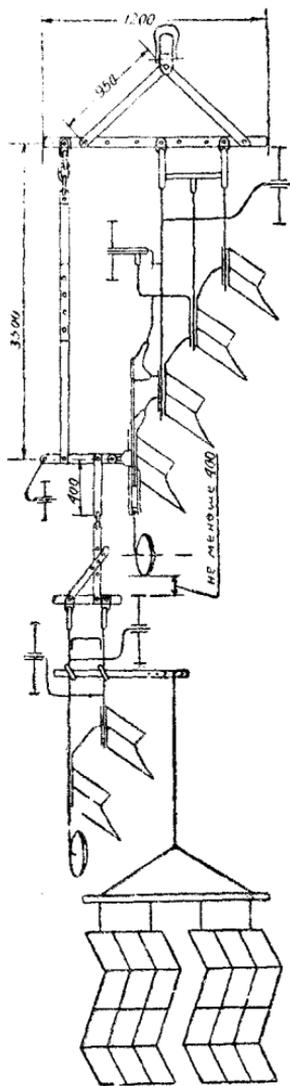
Схема сцепки 4-корпусного и 2-корпусного тракторных плугов с двумя звеньями бороны „зиг-заг“. Рабочая ширина захвата—1,80 м. Агрегат рассчитан на работу с трактором СХТЗ-НАТИ.
